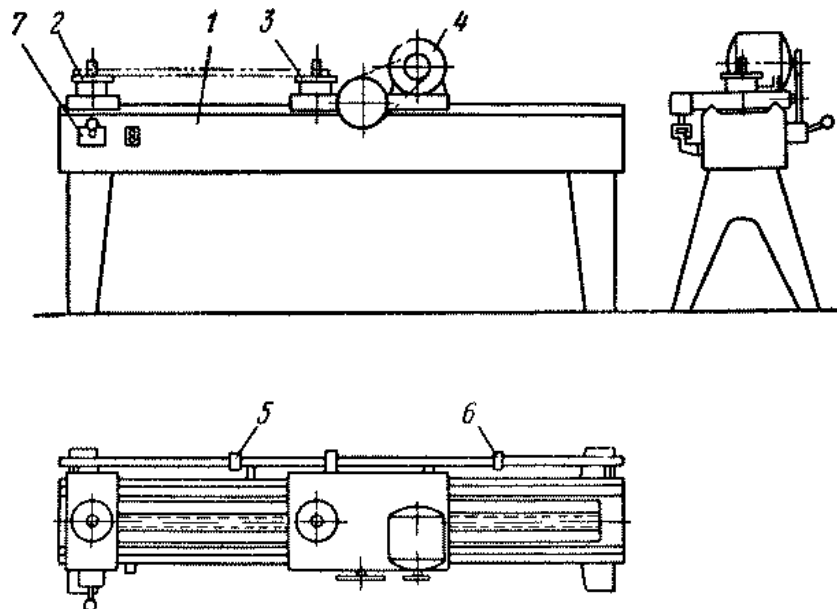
Станок для растяжки круговой заготовки статорных катушек.
